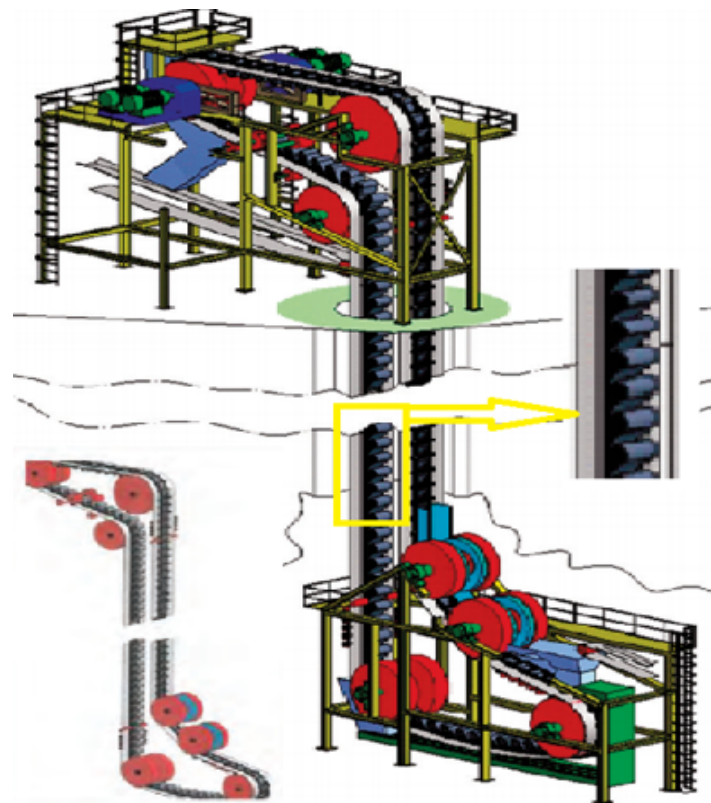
Общий вид ковшового элеватора системы Pocketlift
